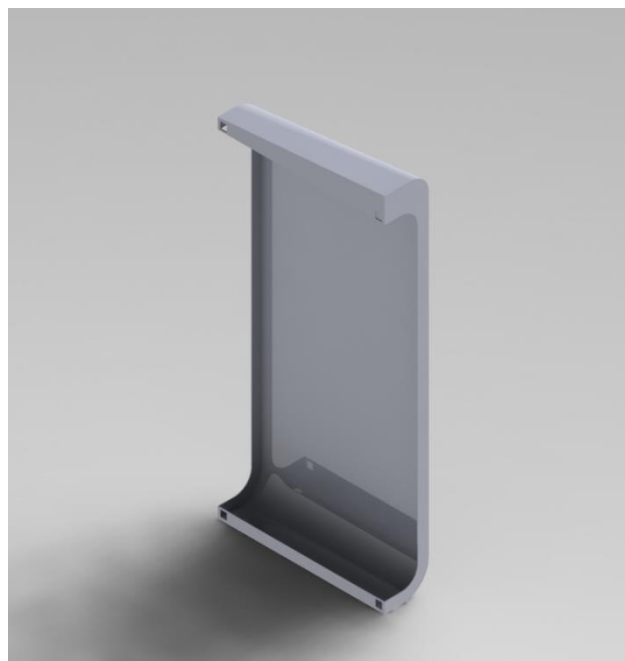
Ensamblaje subconjunto 1.2. Soldadura 5, 6, 7 y 8.
